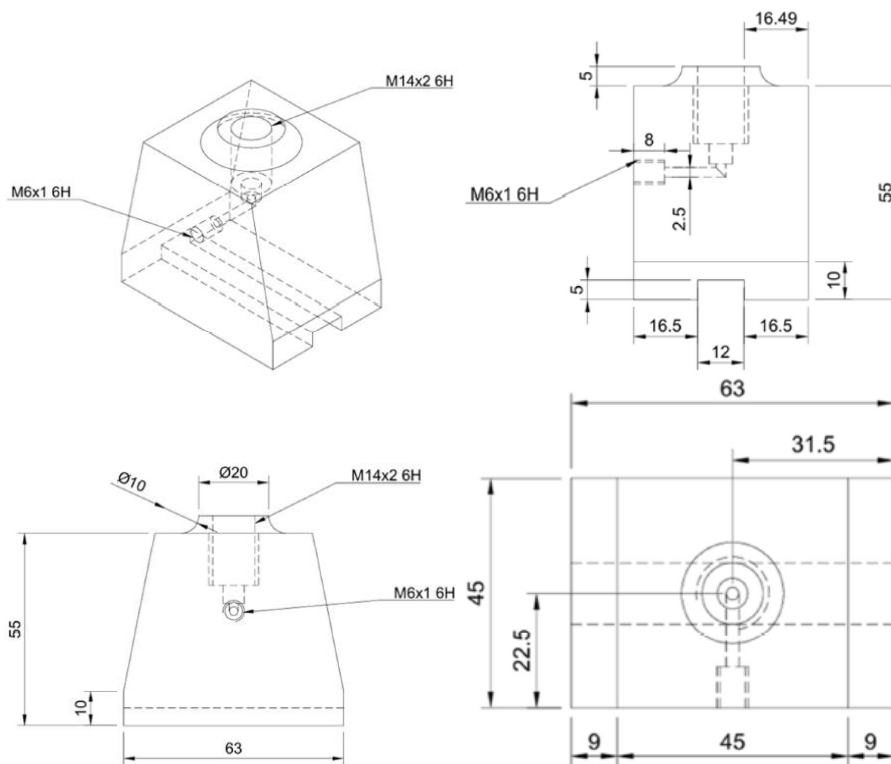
Dimensiones del adaptador acoplador de probeta y mordazas de la máquina.
